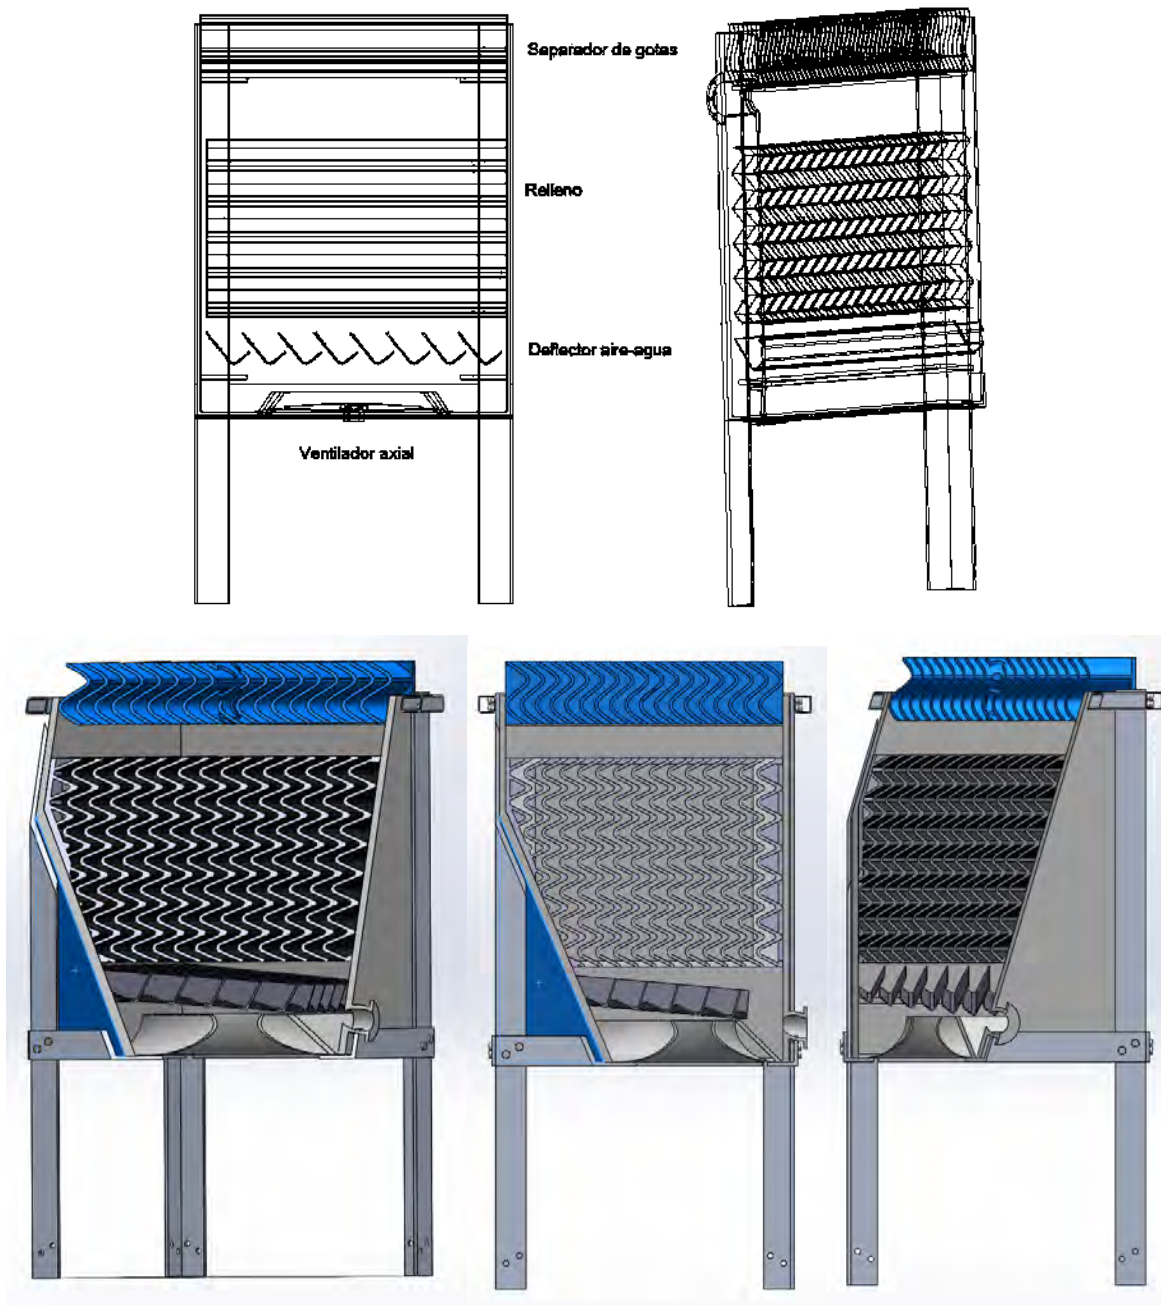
Vista de sección bajo perspectiva en alzado, vista lateral y con Angulo de 30 grados de los componentes en el interior de la torre de tiro forzado a contraflujo.
